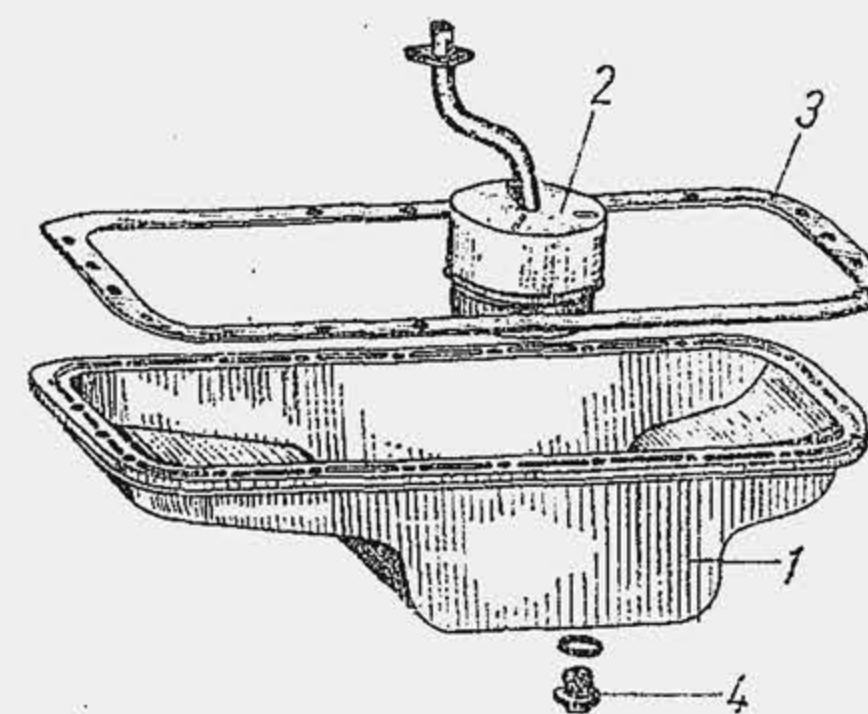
Carterul inferior al motorului ARO-L 25.
